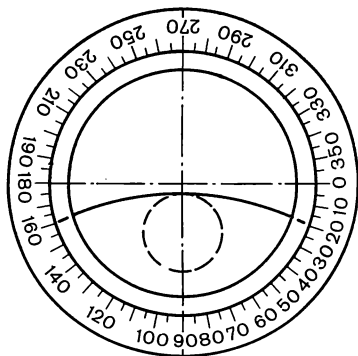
Установка бифокальных линз на поворотном-разметочном столе станка для обрезаки очковых линз.
